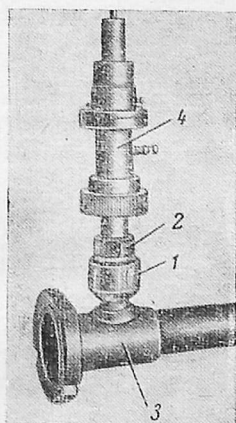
Внешний вид сварного грибка со вставленным в него надетателем.
